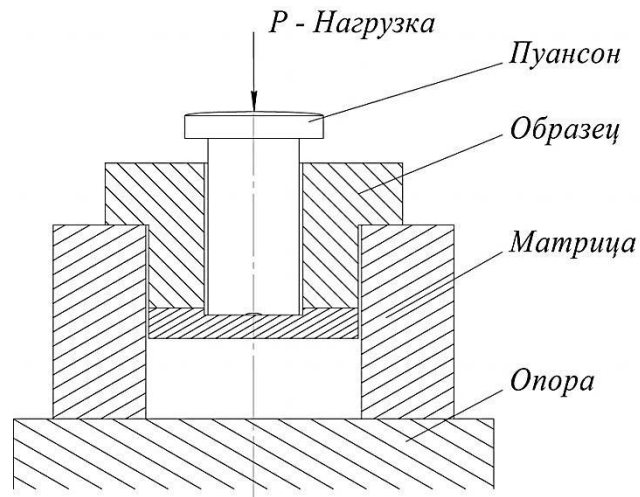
Схема приспособления для испытаний на отрыв лакирующего слоя
